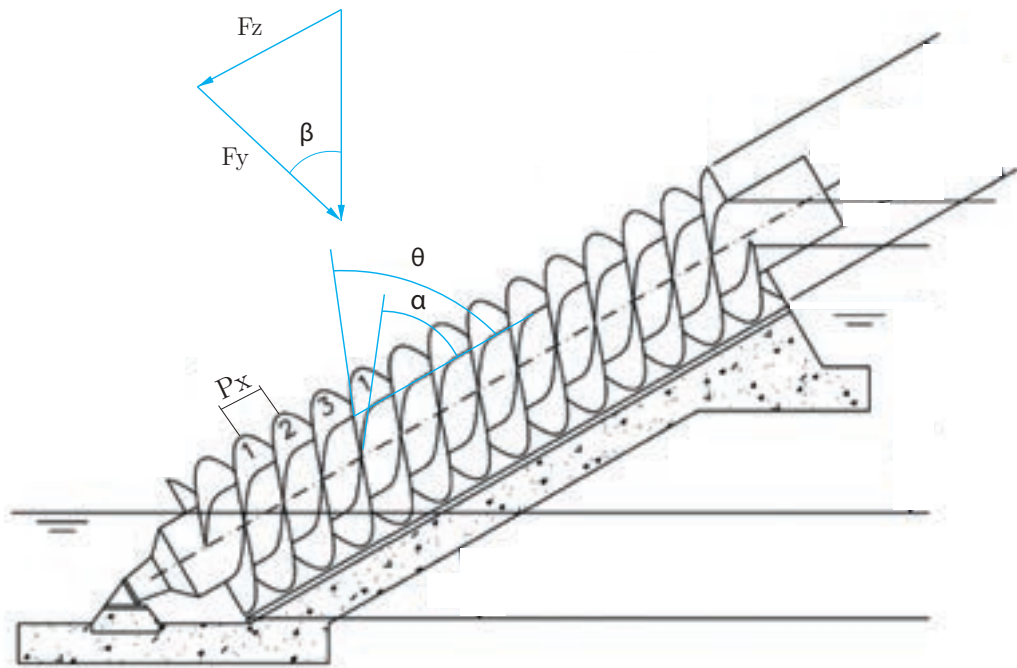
Plano "z - y" del tornillo. Fuente: [29]
